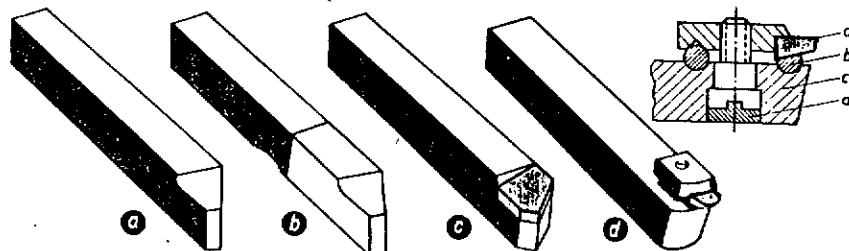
Herramientas para torneear. a) Herramienta de corte hecha completamente de acero rápido (herramienta de una pieza); b) parte cortante de acero rápido soldada a tope; c) placa de acero rápido sobrepuesta mediante soldadura a placa de metal duro nuda mediante fusa soldadura; d) diamante con pieza porta-diamante (a, diamante; b, cañee; c, pieza portadiamante; d, empaste).
